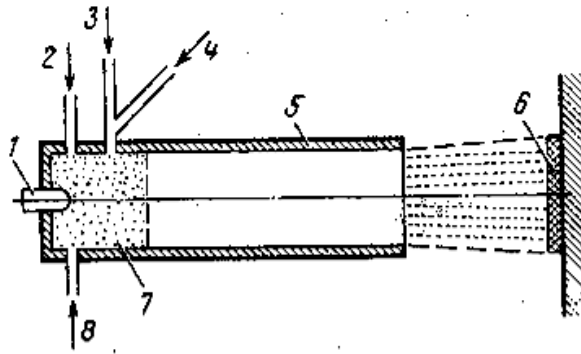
Схема детонаційного напилювання: 1 – електрична свічка; 2 – подача кисню; 3 – продування азотом; 4 – подача порошку; 5 – цівка; 6 – напилений метал; 7 – камера вибуху; 8 – подача ацетилену
